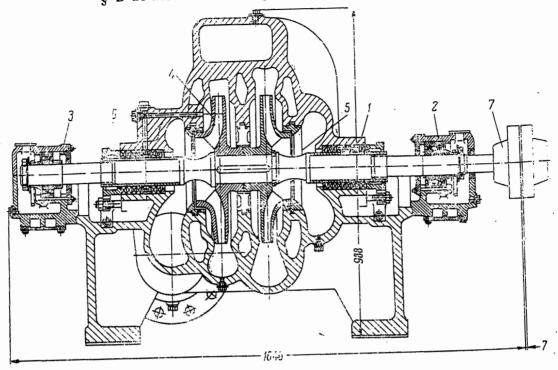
Центробежный насос 3В-200 $\times$ 2. 1— корпус; 2— подшипник опорно-упорный; 3— подшипник опорный; 4— ротор; 5— уплотнения; 6— букса сальника; 7— муфта упругая.
